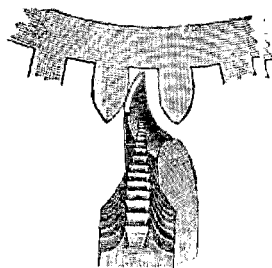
Установка заднего конца поводка при толстом фрезере.
